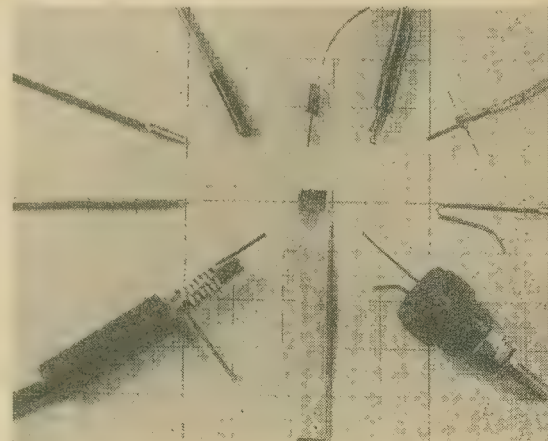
Werkzeug zum Lösen von Wendelbuchsen an schwer zugänglichen Stellen im Einsatz
